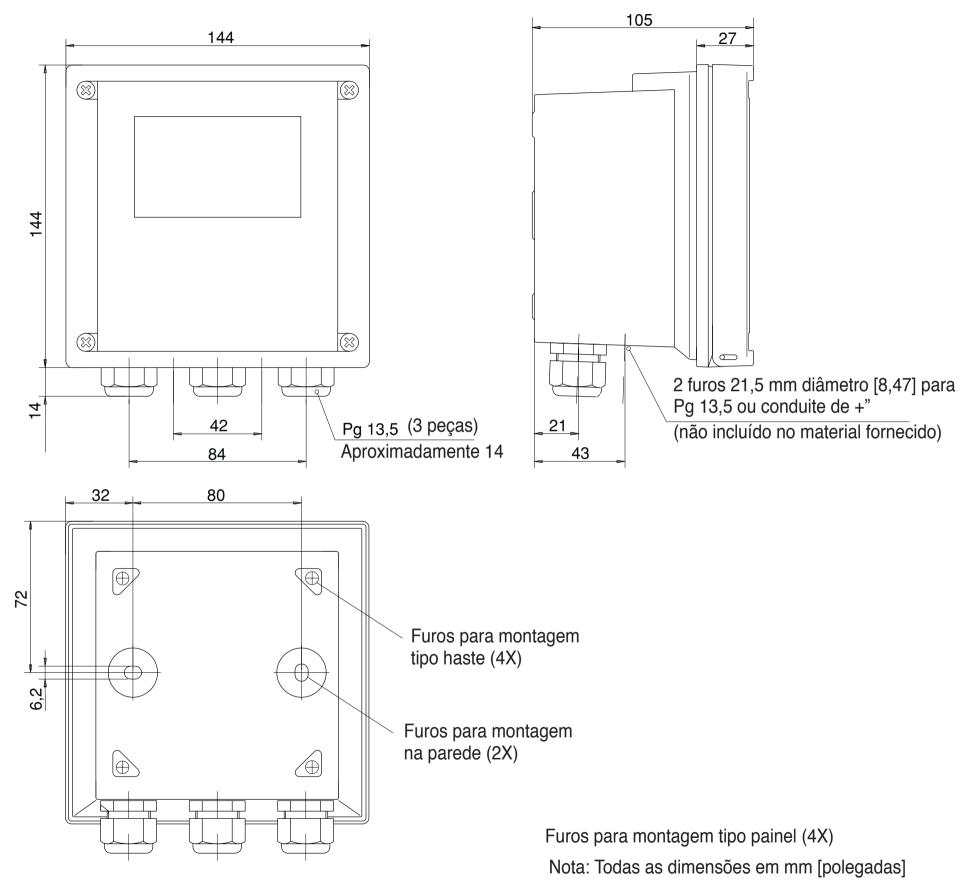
Desenho das dimensões do Transmissor e diagrama de montagem
